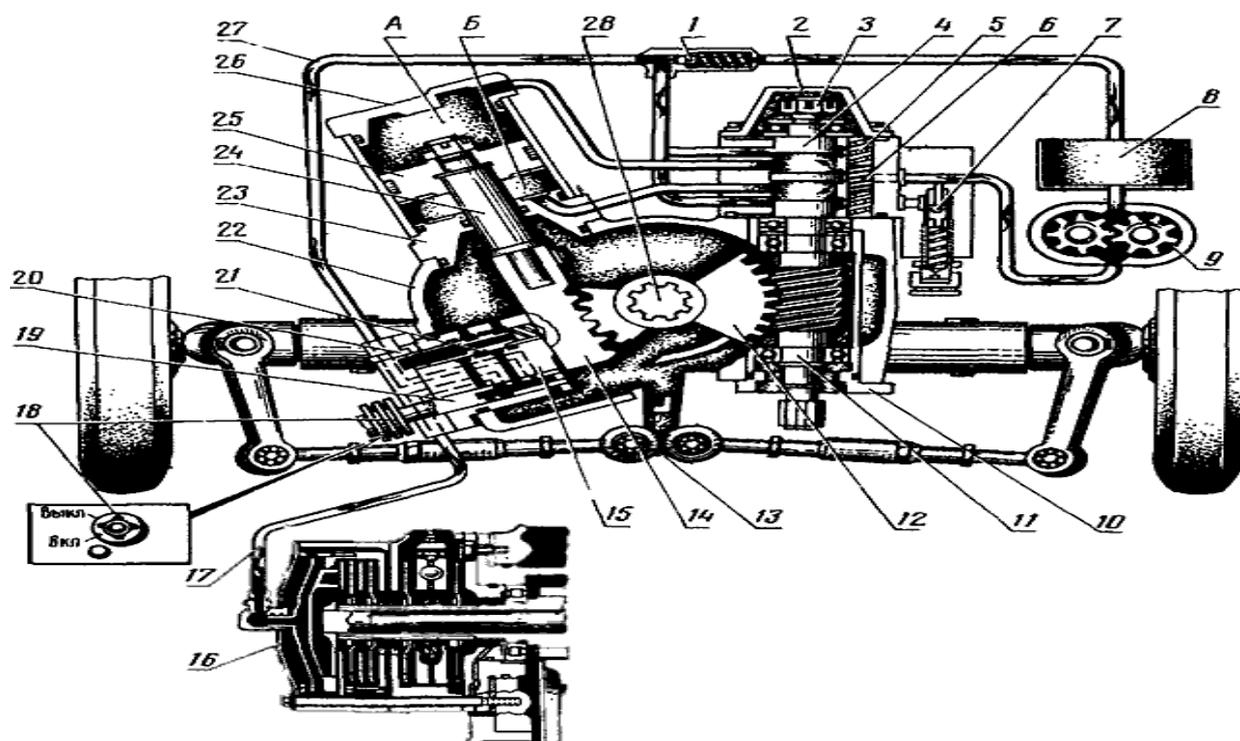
Схема работы гидроусилителя рулевого управления и блокировки дифференциала: А - бесштоковая полость; Б - штоковая полость цилиндра; 1 - редукционный клапан; 2 - крышка распределителя; 3 - гайка; 4 - золотник; 5 - ползун; 6 - центрирующая пружина; 7 - предохранительный клапан; 8 - фильтр; 9 - насос; 10 - эксцентричная втулка; 11 - червяк; 12 - сектор; 13 - сошка; 14 - рейка; 15-упор шейки; 16 - цилиндр блокировки; 17 - маслопровод датчика; 18- маховичок крана; 19 - кран датчика; 20 - щуп; 21 - золотник датчика; 22 - корпус гидроусилителя; 23 - задняя крышка цилиндра; 24 - шток; 25 - поршень; 26 - передняя крышка цилиндра; 27 - маслопровод клапана блокировки; 28 - поворотный вал.
